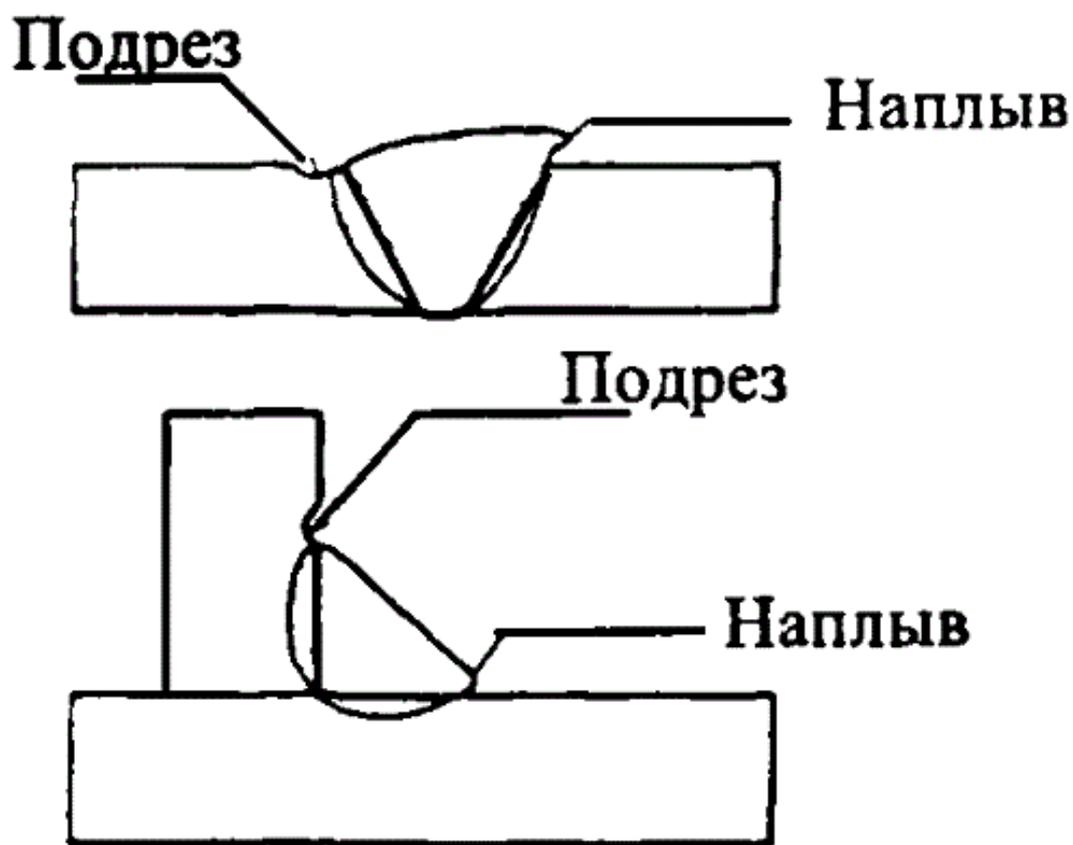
Подрез и наплыв в сварном соединении
